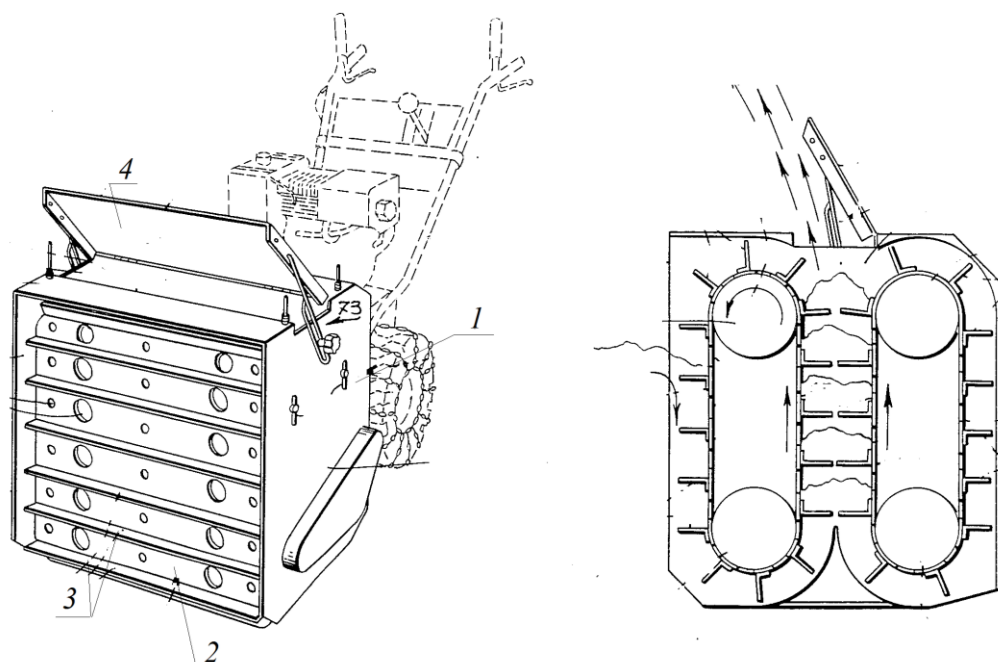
Принципиальная схема снегоочистителя с каналом для снега из вертикальных скребков с полосами, где 1 – корпус; 2 - лента; 3 – горизонтальный скребок; 4 – верхняя крышка
